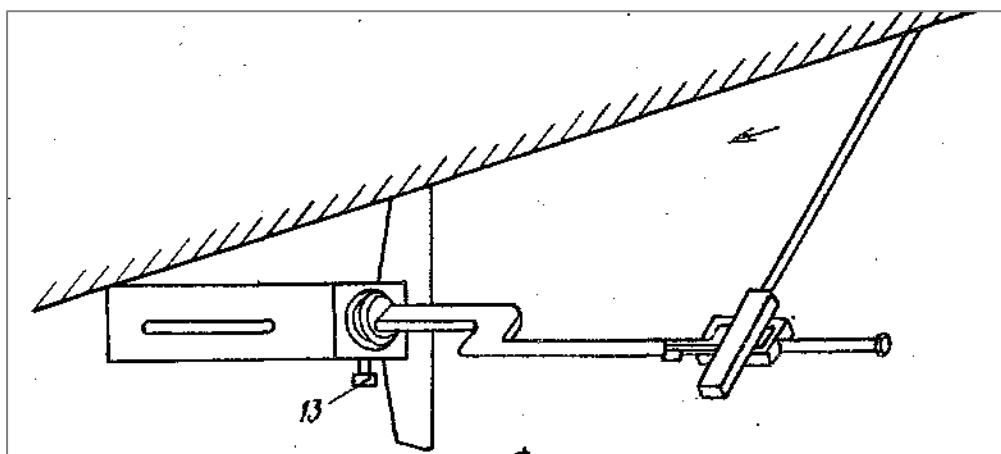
б – Устройство для сварки наклонным электродом
